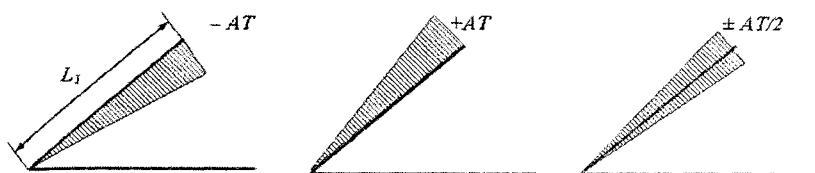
Схемы расположения полей допусков углов призматических деталей
